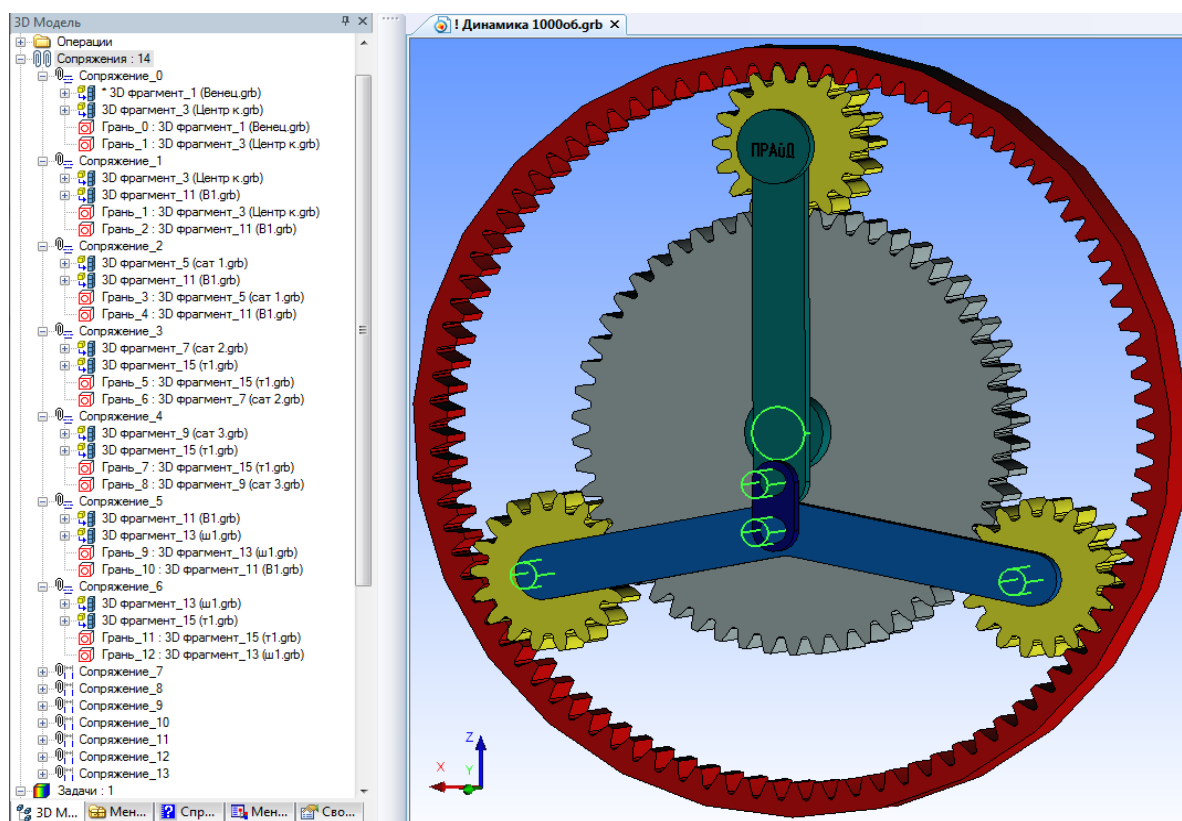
Сборка трёхсателлитного планетарного механизма
